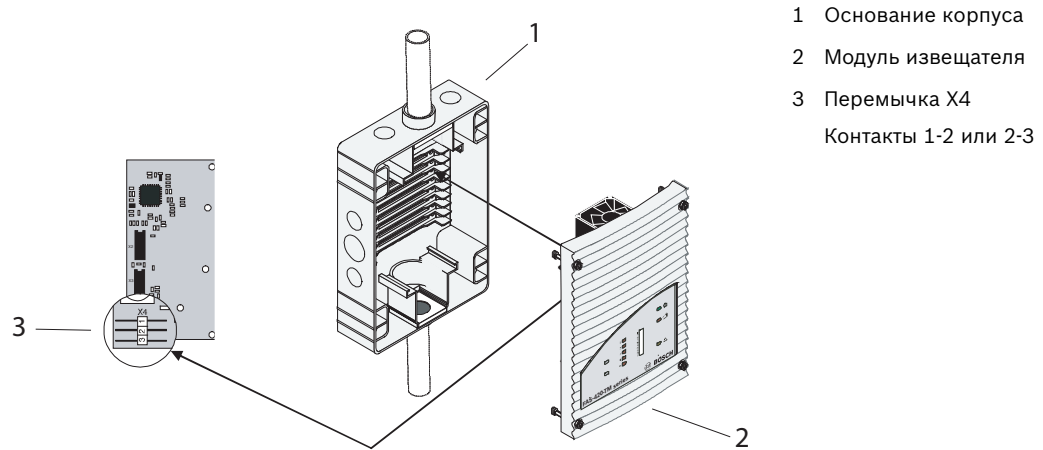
Установка модуля извещателя в основание корпуса
